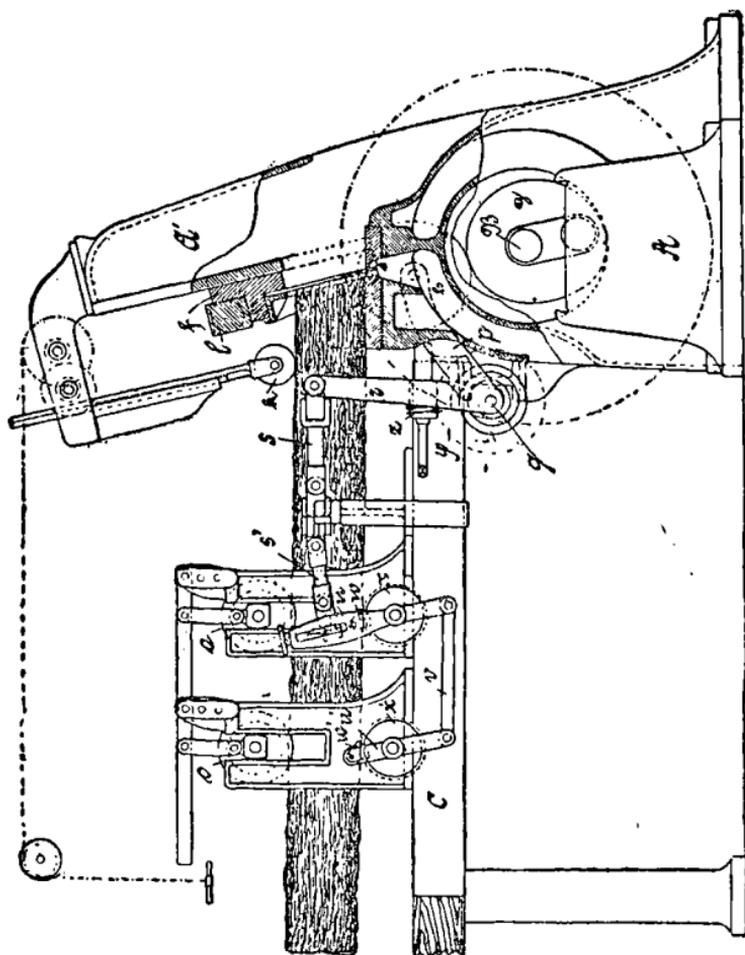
Machine à déchiqueter de Niethammer, vue de côté.
